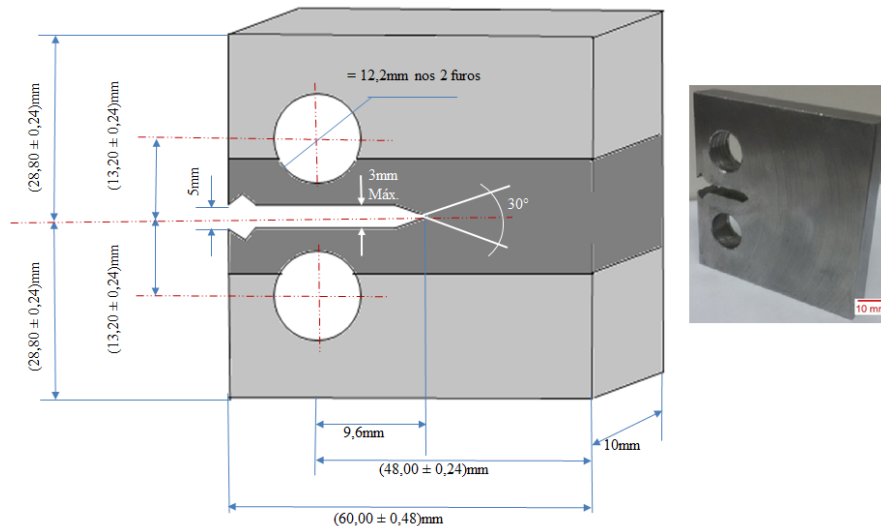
Representação esquemática das dimensões do corpo de prova CT e detalhe da peça usinada.
